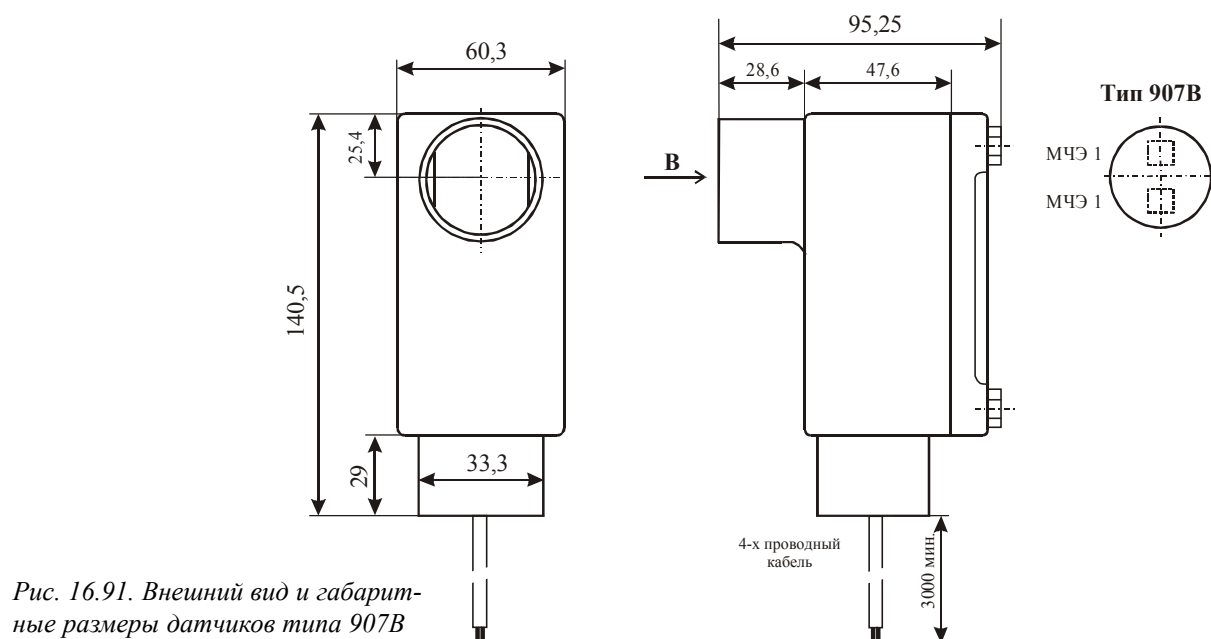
Внешний вид и габаритные размеры датчиков типа 907В
